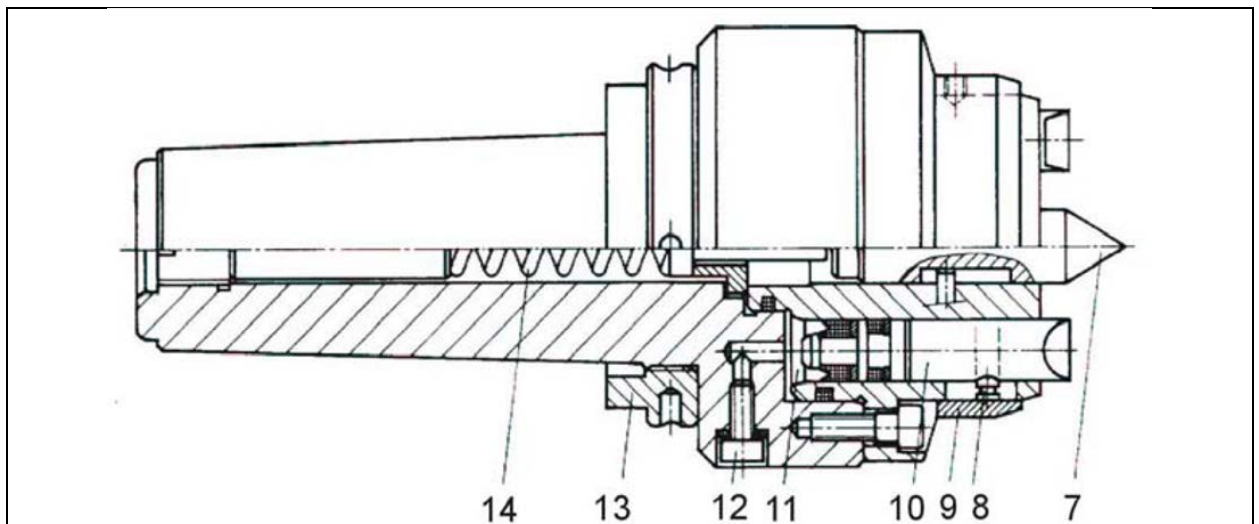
Повідковий патрон з плаваючим центром і торцевими штирями для передачі крутного моменту
